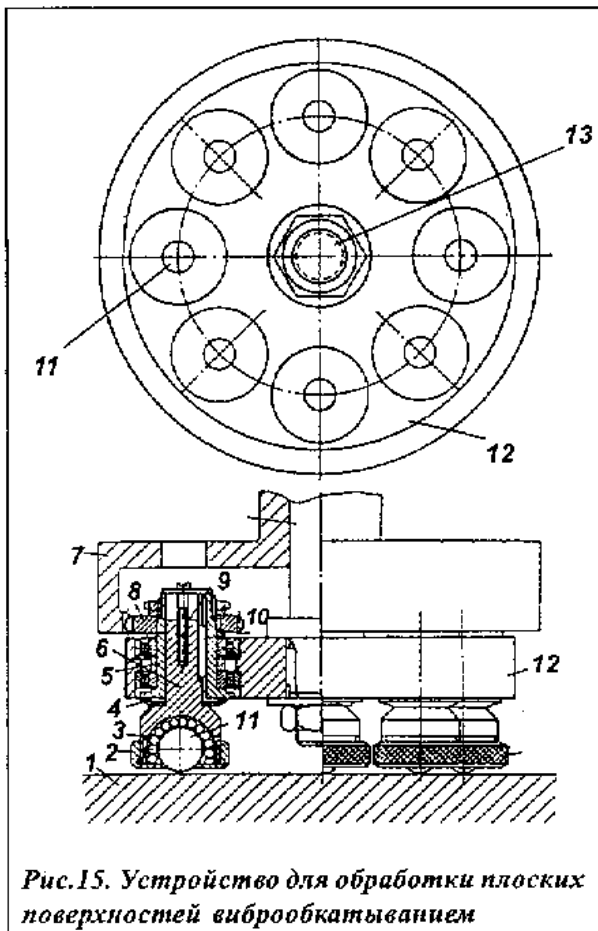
Устройство для обработки плоских поверхностей виброобкатыванием
